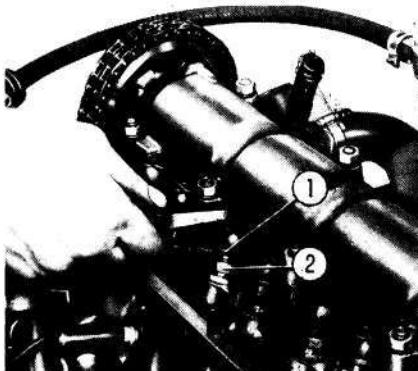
Регулировка зазоров в механизме привода клапанов: 1 — регулировочный болт; 2 — контргайка регулировочного болта
